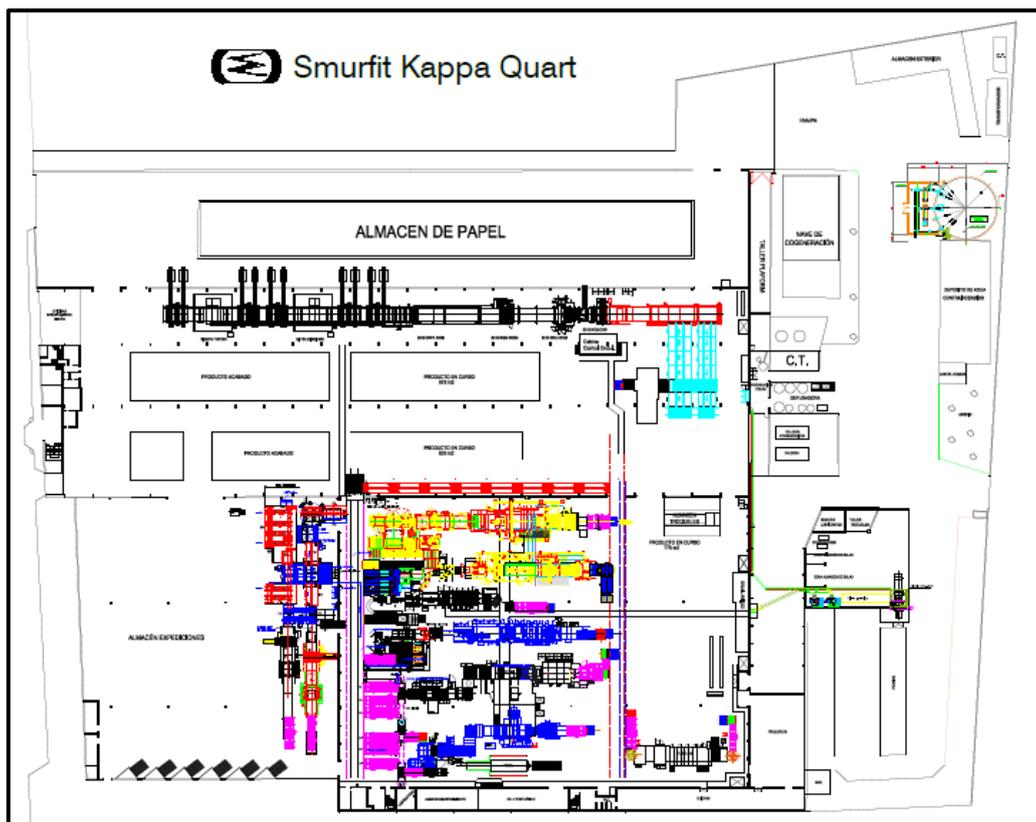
Plano general de la planta de Smurfit Kappa Quart
